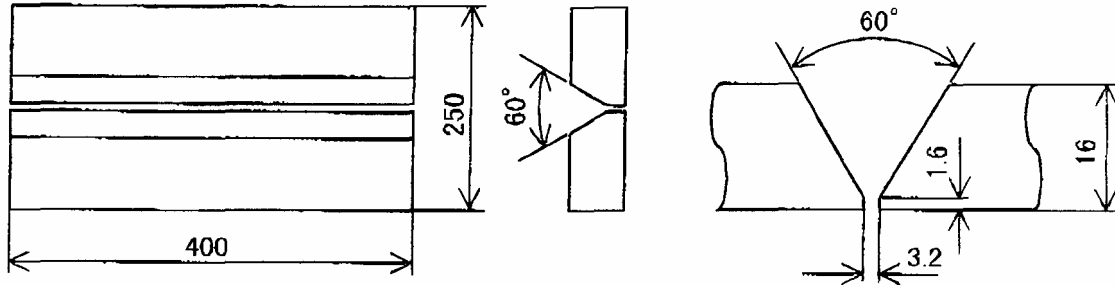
Габаритные размеры и подготовка кромок испытываемого образца
